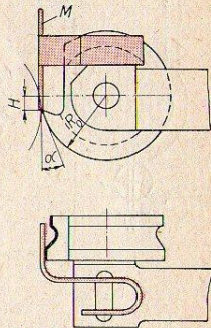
Držák kotoučového nože pro zadní suport automatu
